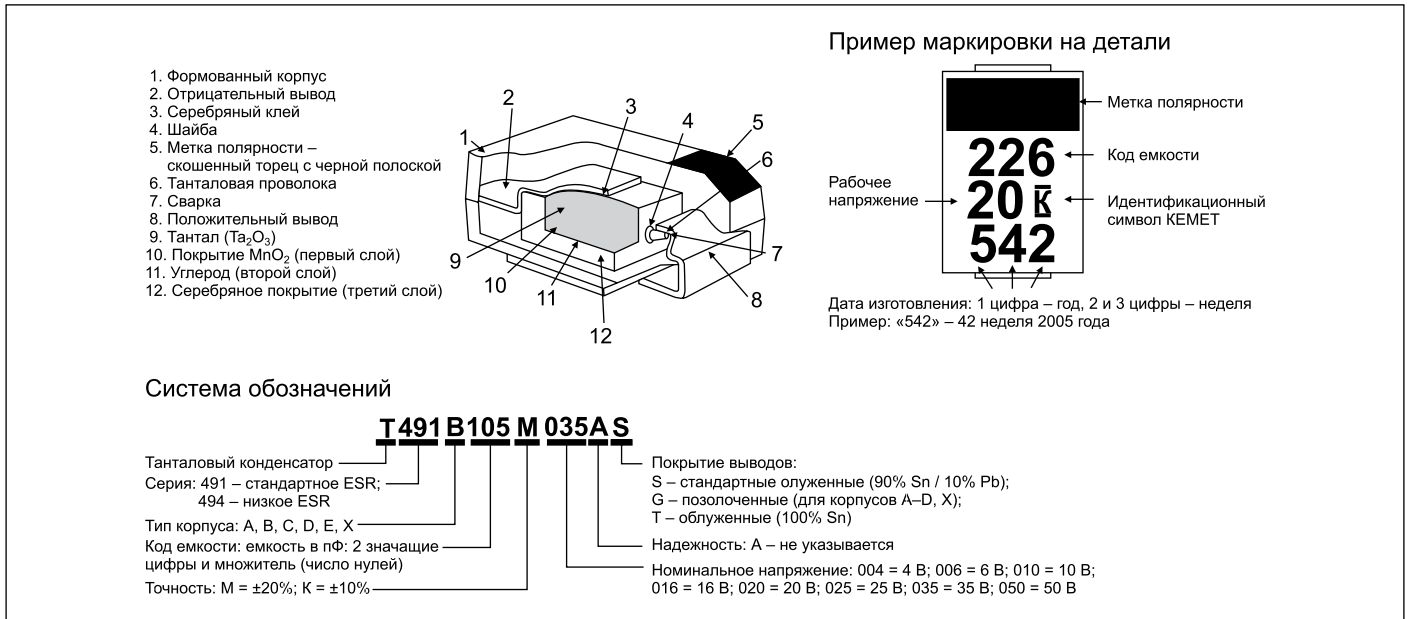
Маркировка и система обозначений танталового конденсатора для поверхностного монтажа
